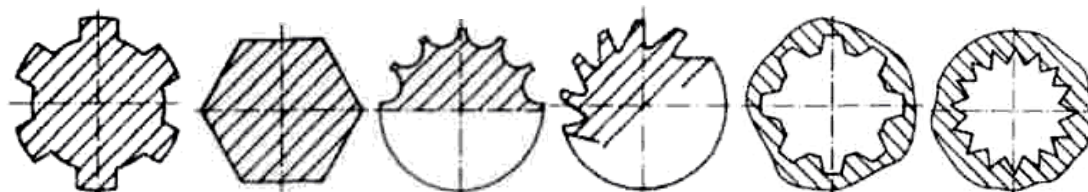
Эскизы профилей деталей обрабатываемых методом обката
